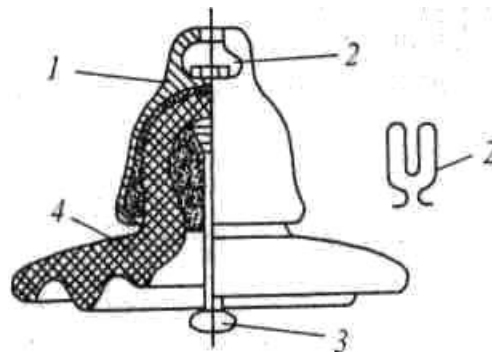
Підвісний ізолятор: 1 — шапка; 2 — замок; 3 — стержень; 4 — тарілка
